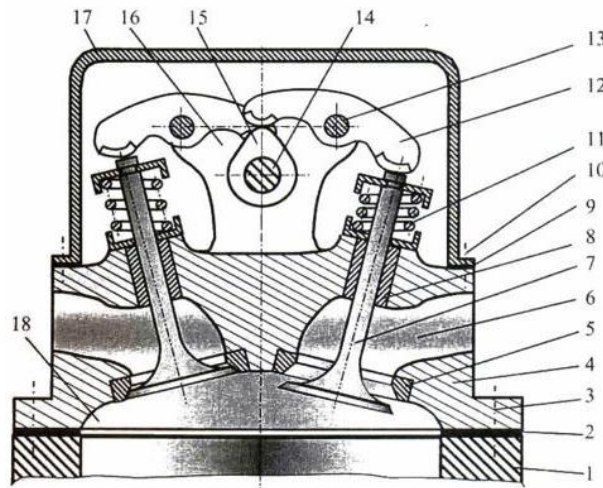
Конструкція головки блока циліндрів: 1 – блок циліндрів, 2 – прокладка блока, 3 – кріплення головки до блока, 4 – корпус головки блока, 5 – сидло клапана, 6 – впускна (випускна) порожнина, 7 – впускний (випускний) клапан, 8 – напрямна клапана, 9 – прокладка кришки, 10 – кріплення кришки, 11 – пружина, 12 – штовхач, 13 – вісь важеля, 14 – розподільний вал, 15 – кулачок розподільного валу, 16 – корпус розподільного валу, 17 – кришка, 18 – камера згорання
